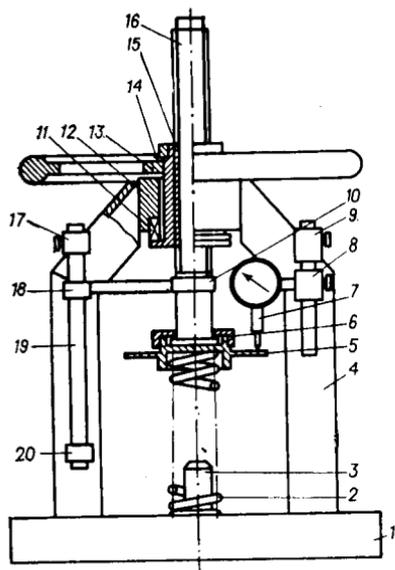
Приспособление для испытания пружин предохранительных клапанов: 1 — основание; 2 — пружина; 3 — палец; 4 — стойка; 5 — специальная крышка; 6, 14 — накидные гайки; 7 — индикатор; 8, 9, 12, 17, 18, 20 — втулки; 10 — хомут; 11 — упорный подшипник; 13 — маховик; 15 — вращающаяся гайка; 16 — шпиндель; 19 — штанга.
